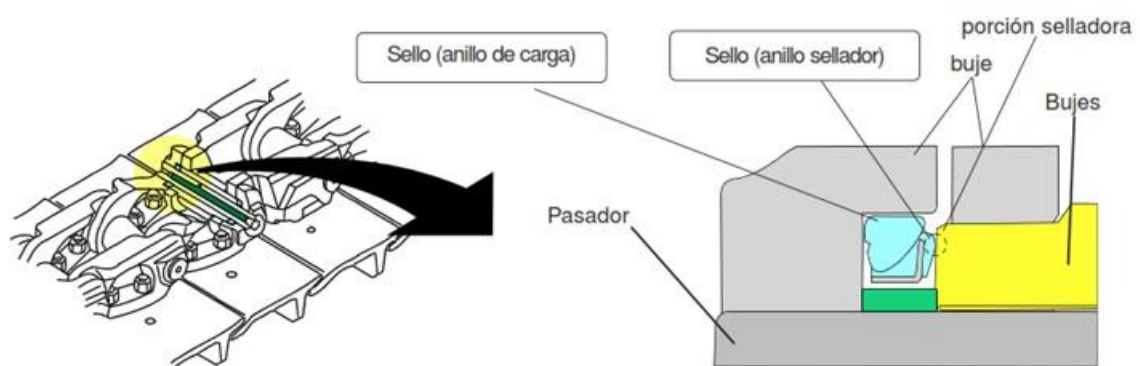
Apoyo de apoyo conjunto pasador y rueda dentada
